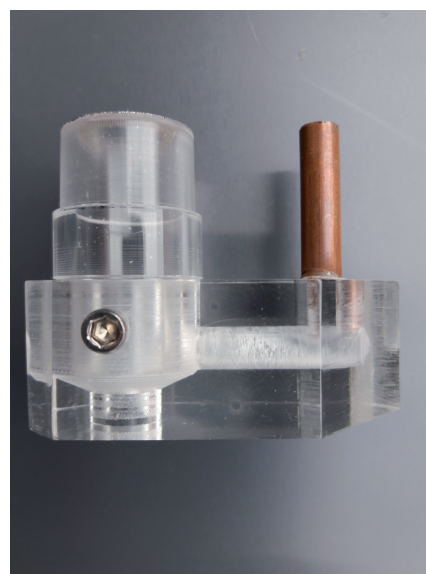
Assemblage avec la vis (photo : F. Benoit).
